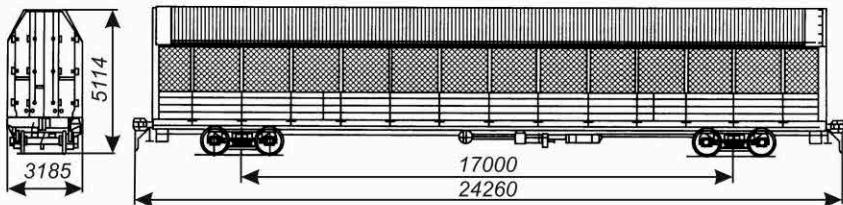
Крытый двухярусный вагон для легковых автомобилей модели 11-287
